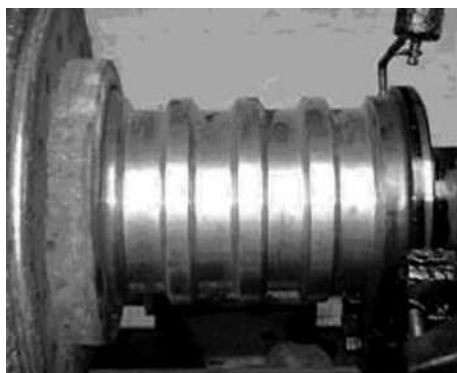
Guiño del eje de maza superior maquinado y recuperado por soldadura
